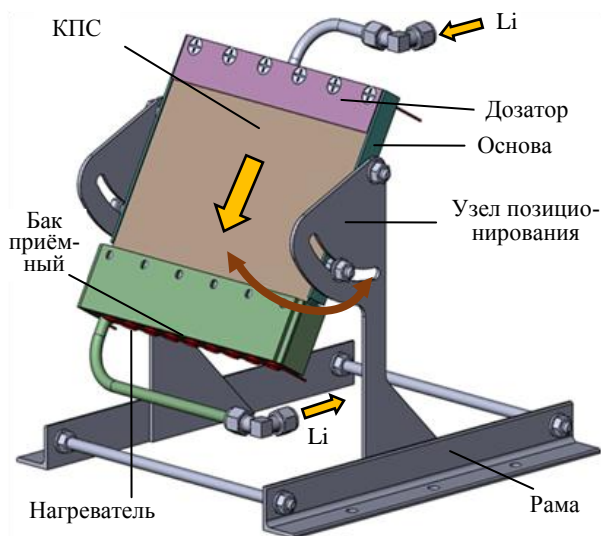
Внешний облик макета диверторной мишени токамака Т-15МД
